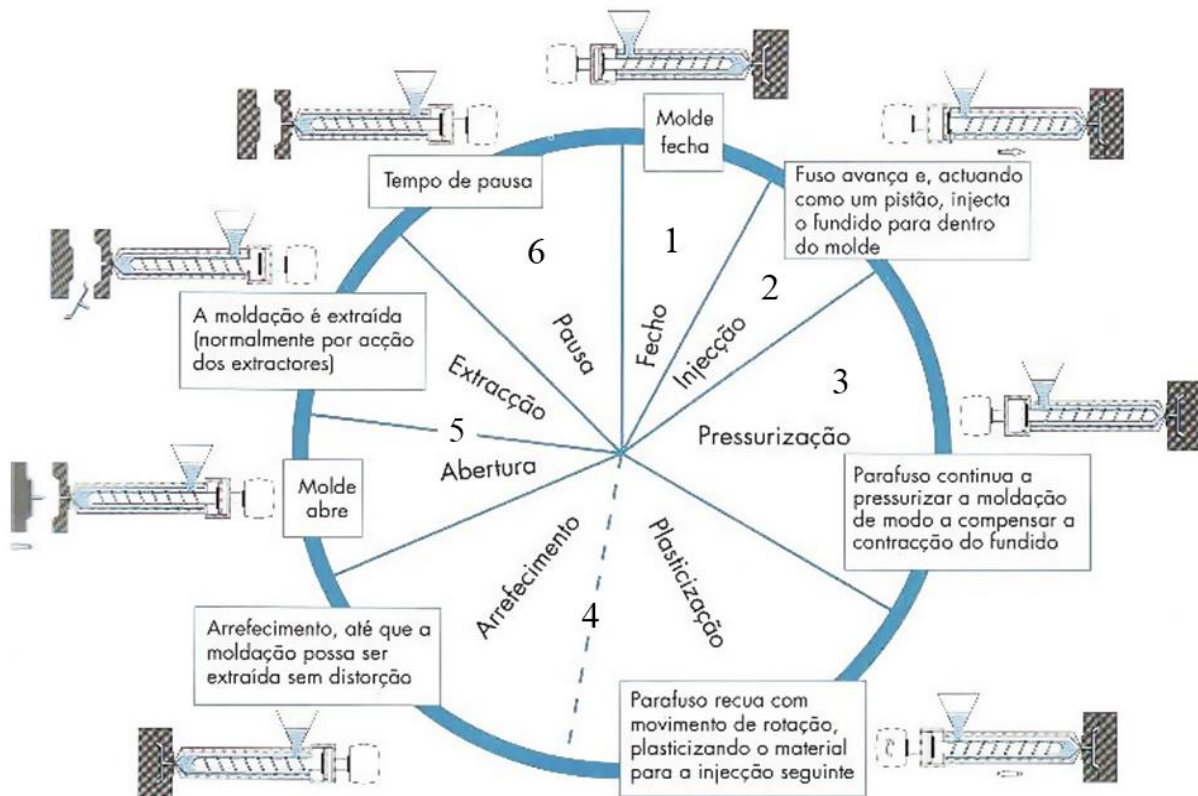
Ciclo de moldação por injeção. Adaptado de [3].
